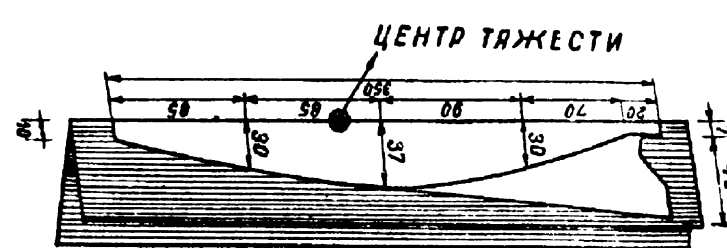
Изготовление чертежа корпуса гидропневматической ракеты
